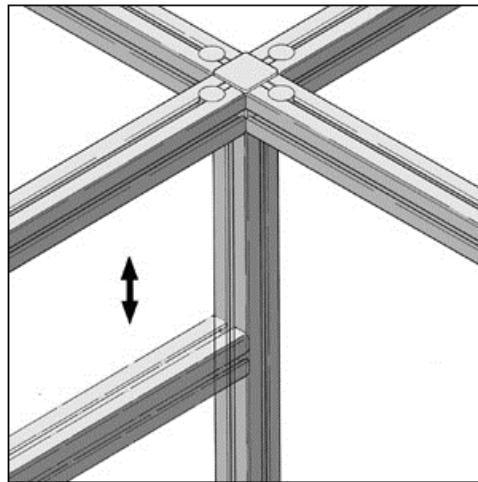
Aplicações de elemento de fixação: *Universal-Fastening Set
